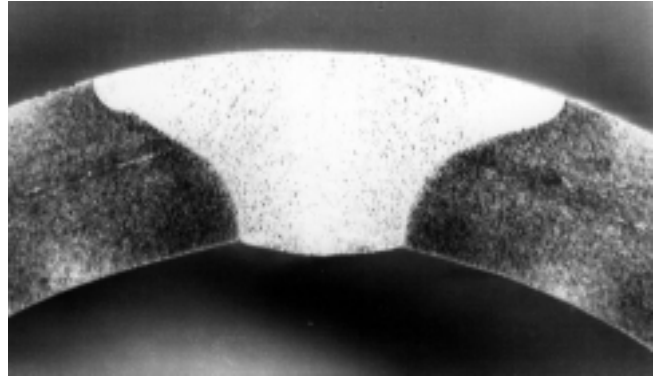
Nahtausbildung beim WIG-Impulslichtbogenschweißen mit höherer Frequenz am Rohr Grundwerkstoff: 1.4301, $t = 2 \text{ mm}$, $v_S = 2,7 \text{ m/min}$, Schutzgas: 95% Ar + 5% H₂, kein Zusatzwerkstoff
